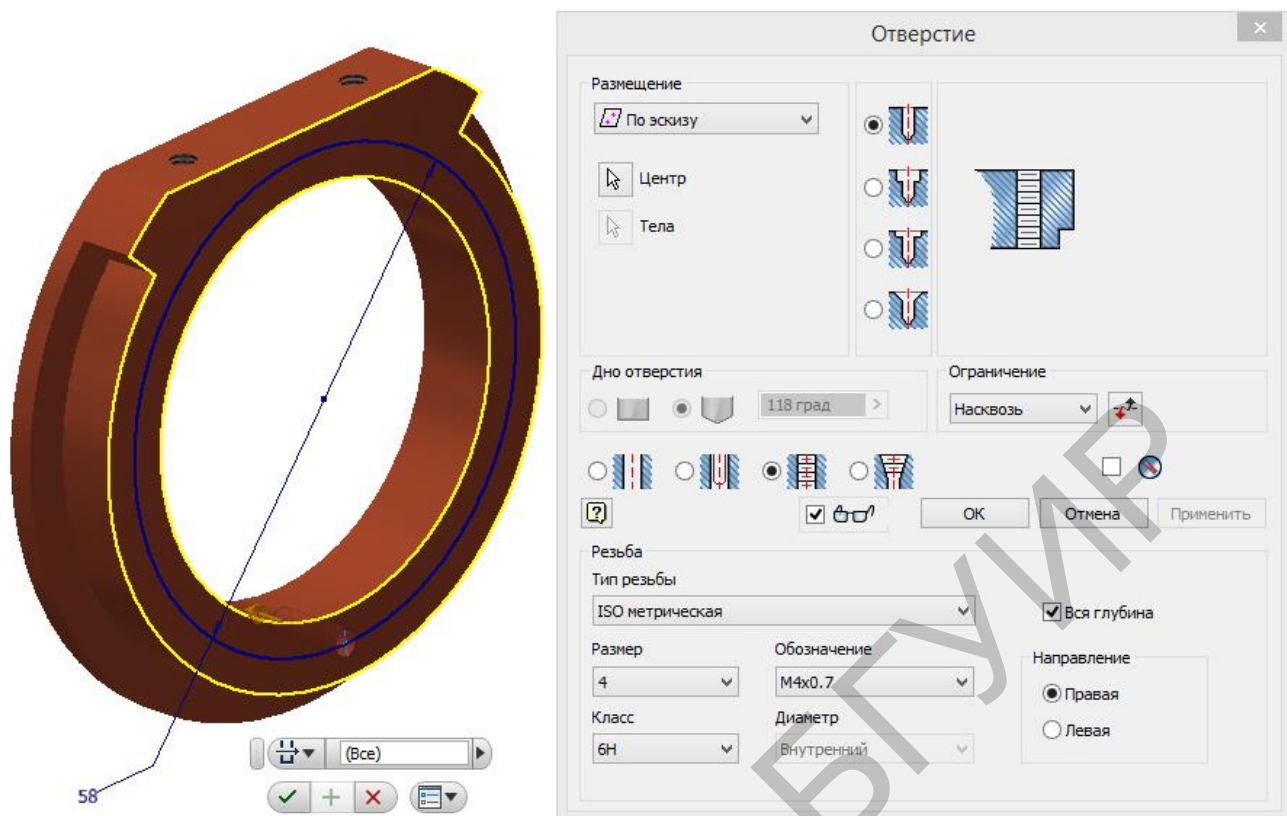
Выполнение одного из трёх сквозных резьбовых отверстий М4 на торце кольца
